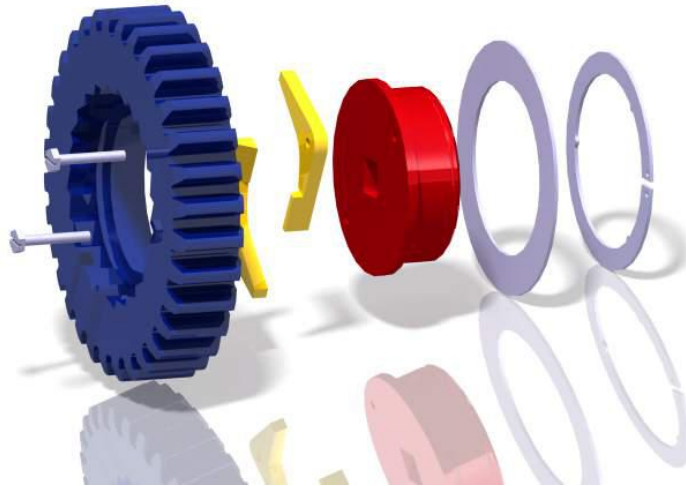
Conjunto corona de transmisión explosionado en sus diferentes piezas.
